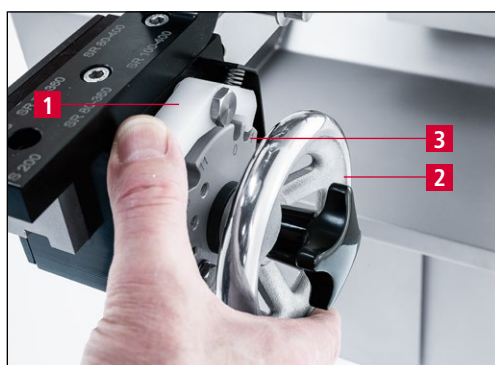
Установка приспособления для заточки в положение заточки «1»
